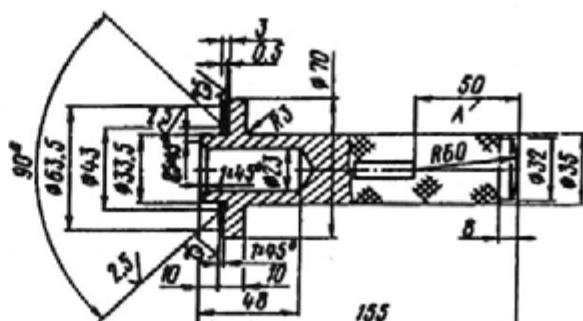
Оправка для запрессовки сальника ведущей шестерни в горловину картера редуктора.
